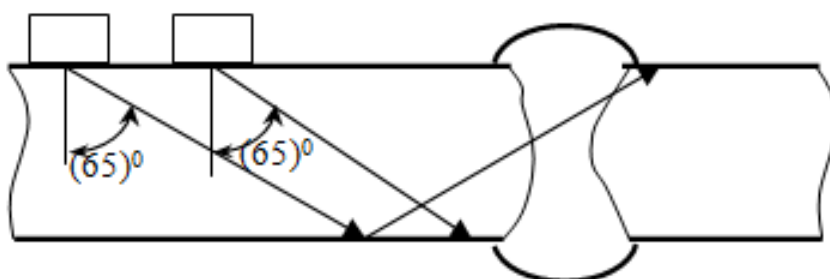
Испытание зоны сварного шва с углом  $60^\circ$
